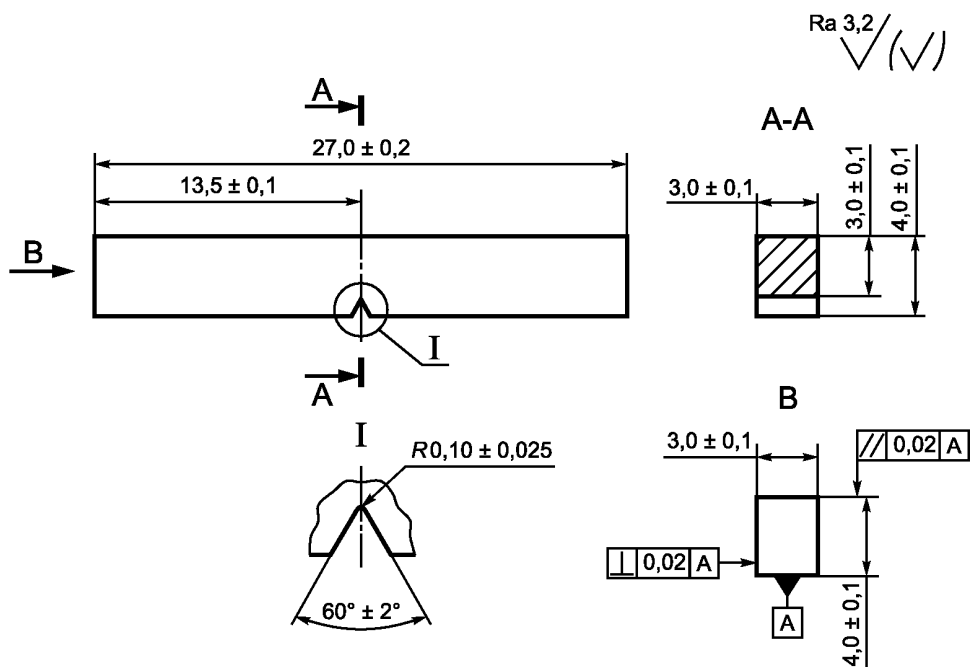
Малоразмерный образец размерами 3×4×27 мм для испытаний на ударный изгиб
